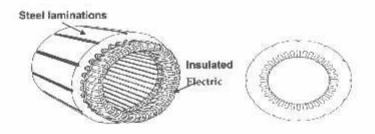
Konstruksi Motor Induksi Theodore Wildi, Electrical Machines, drives, and Power Systems.
